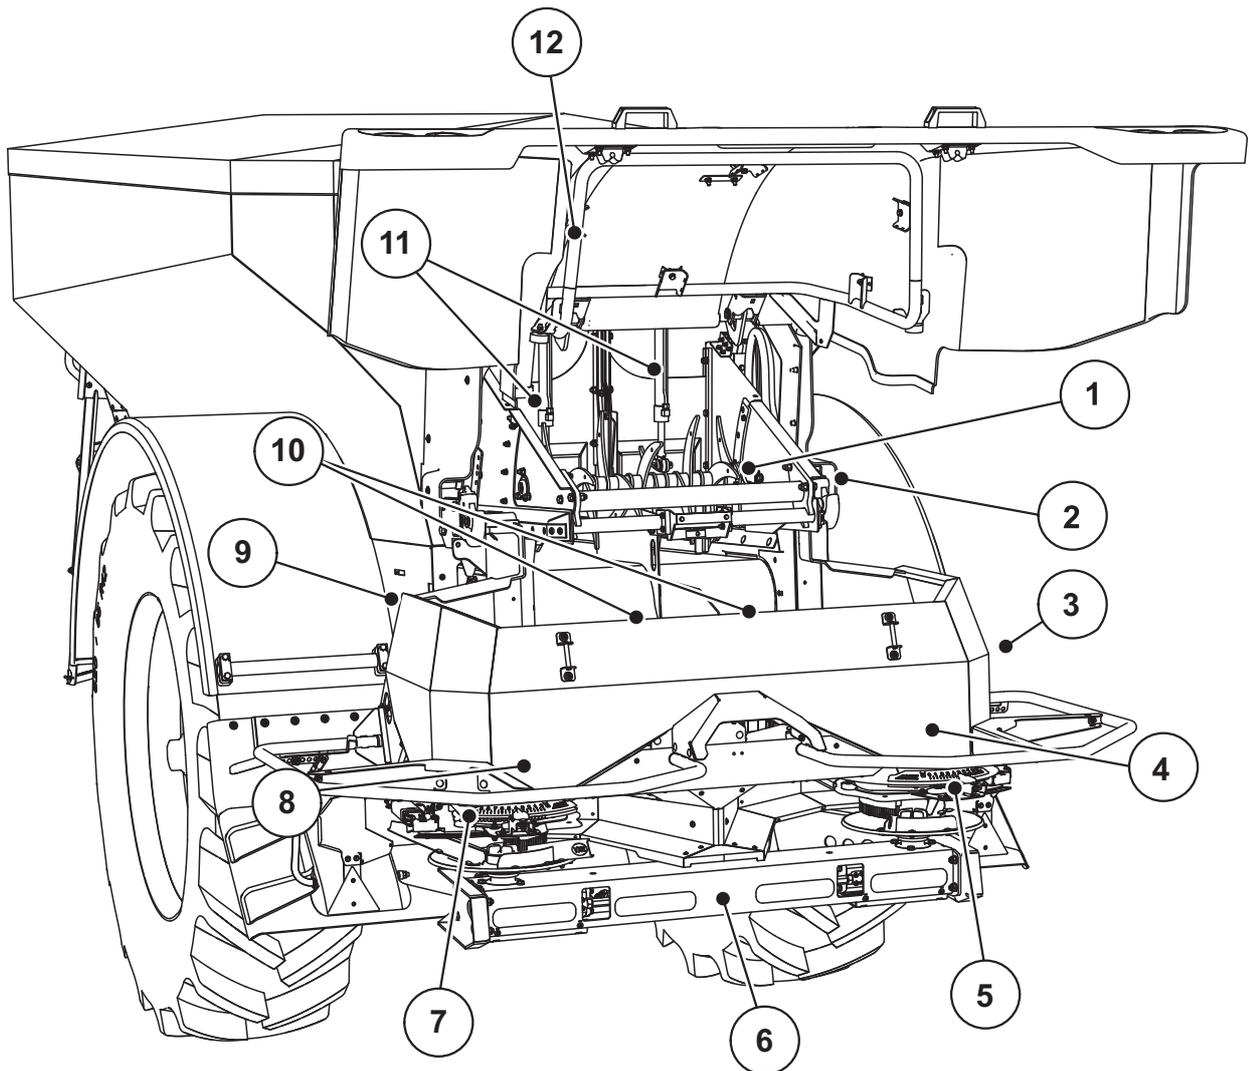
Vue d'ensemble des vérins et capteurs sur l'épandeur pour grandes surfaces AXENT et le dispositif d'épandage d'engrais AXIS-PowerPack
